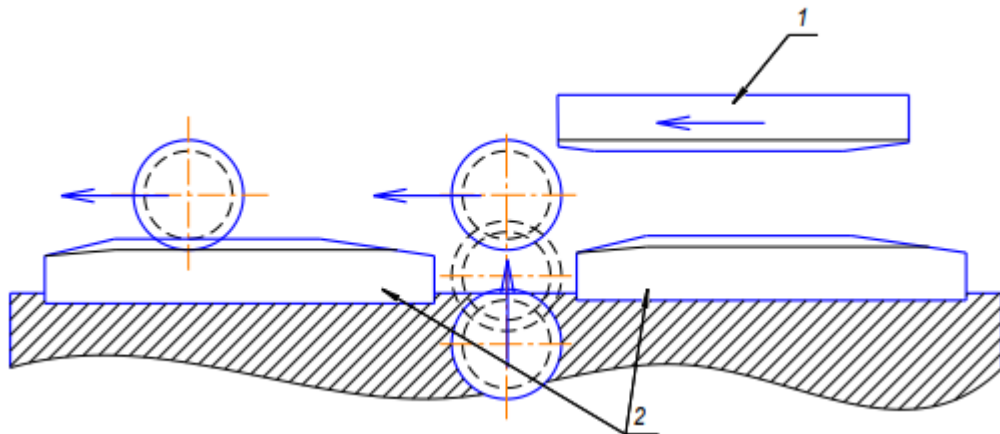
Накатування трьома плашками. Прямий хід: 1 –рухома плашка, 2 – нерухомі плашки
